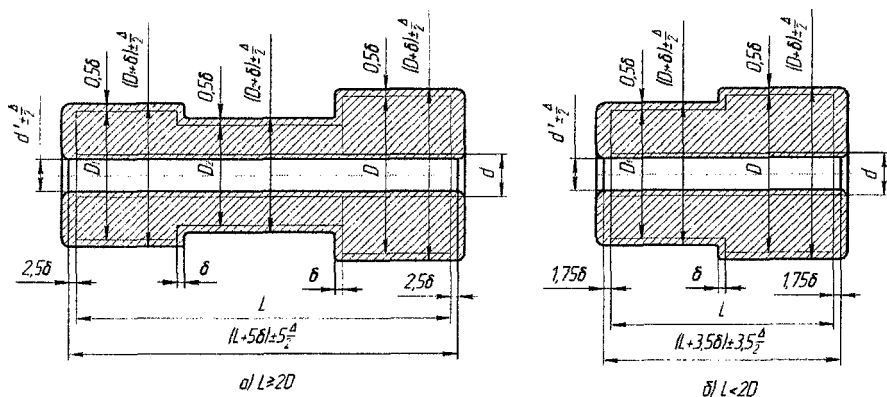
Схема назначения припусков и допусков для поковок 5-ой группы
